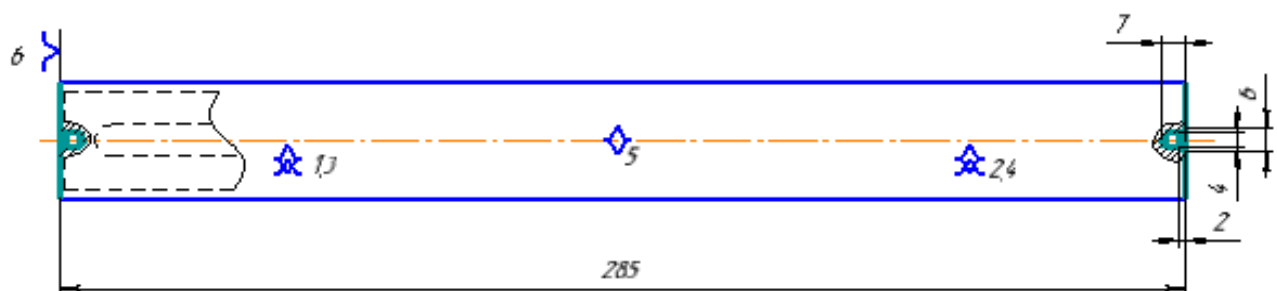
Обробка деталі при фрезерно-центрувальній операції.
